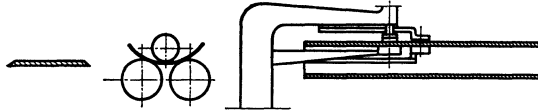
Feuer- bzw. Wassergas-Preßschweißung.
